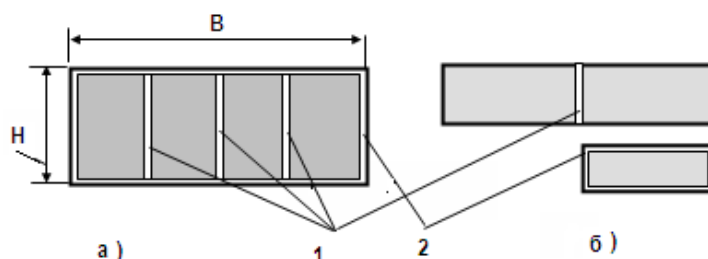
Схемы получения чистовых заготовок (дялянок) из черновых заготовок: а) для толстых досок; б) для тонких досок; 1 - пропилы; 2 - припуски на фрезерование; Н, В – толщина и ширина пиломатериала.
